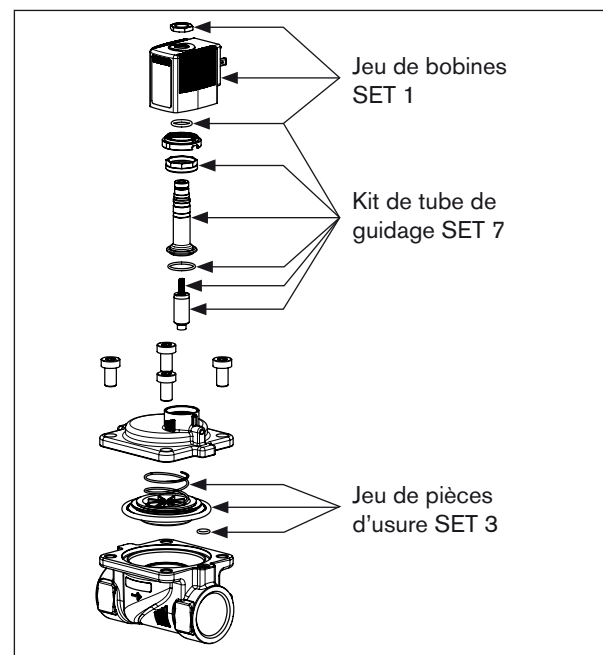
Jeu de pièces de rechange Type 6281 EV
